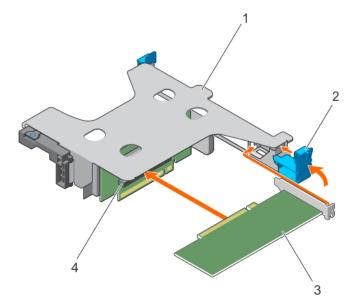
Installation d'une carte d'extension mi-hauteur dans le module de carte de montage double
